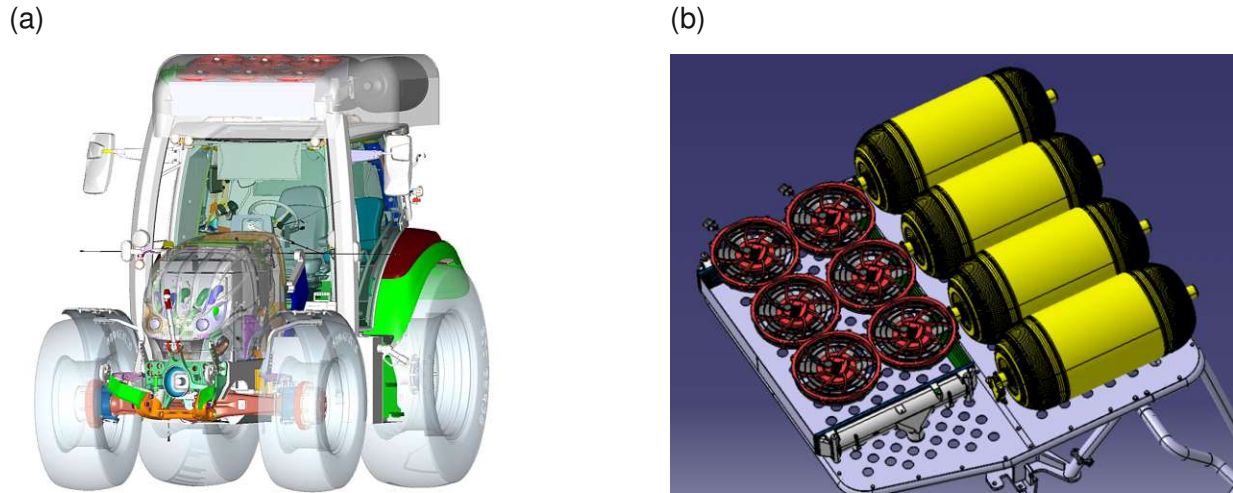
3D-Modell des BZ+EM+CVT-Konzepts mit Dachaufbau (a) und Detailansicht der Rahmenstruktur mit den Wasserstofftanks und Lüftern für den Radiator (b).
